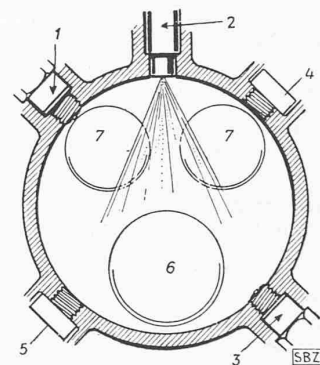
(rechts). Anordnung von Ventilen und Einspritzdüse im Junkers Flugmotor, 1, 3, 4, 5 Kerzengewinde, 2 Einspritzventil, 6 Auslassventil, 7 Einlassventile
